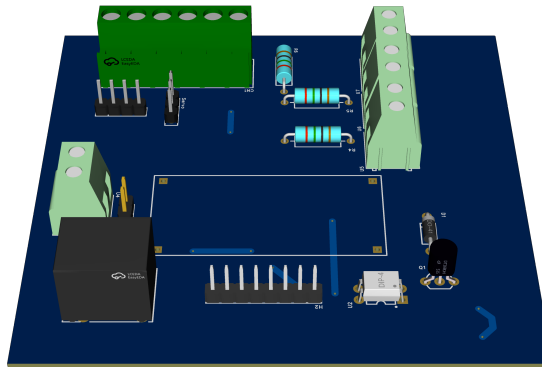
Modelado tridimensional de PCB. Fuente: Autores
